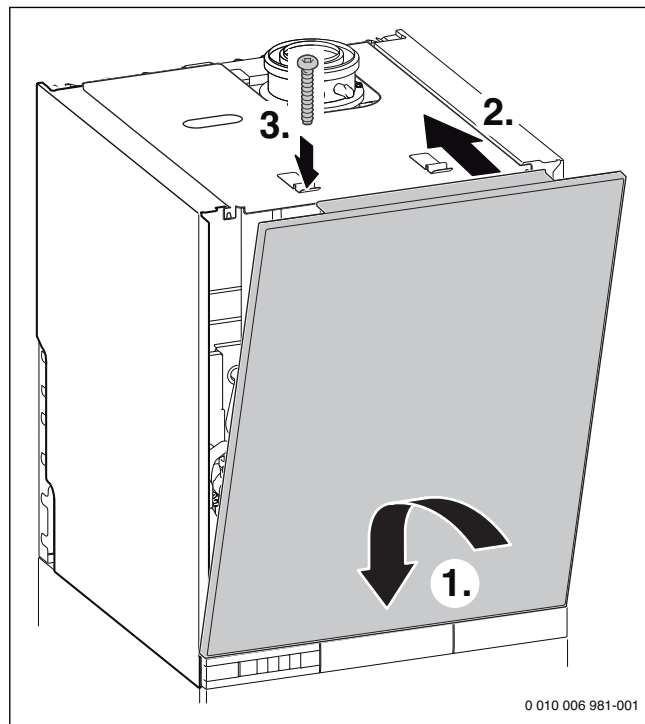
Posuňte horný kryt dozadu a pripevnite ho 4 skrutkami vpredu a vzadu
